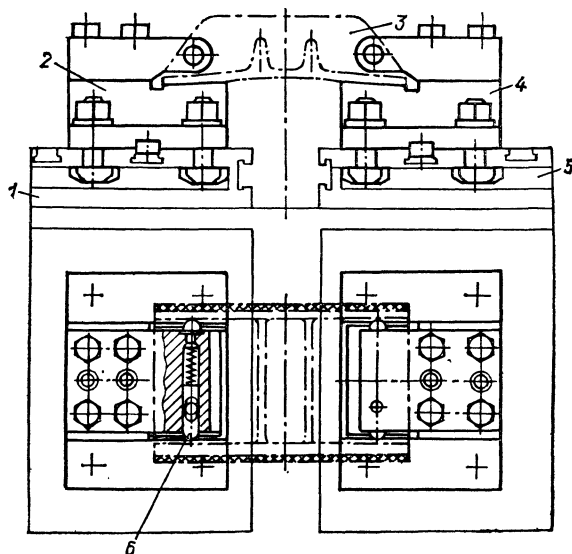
Наладка при фрезеровании двух торцов крышки набором фрез
